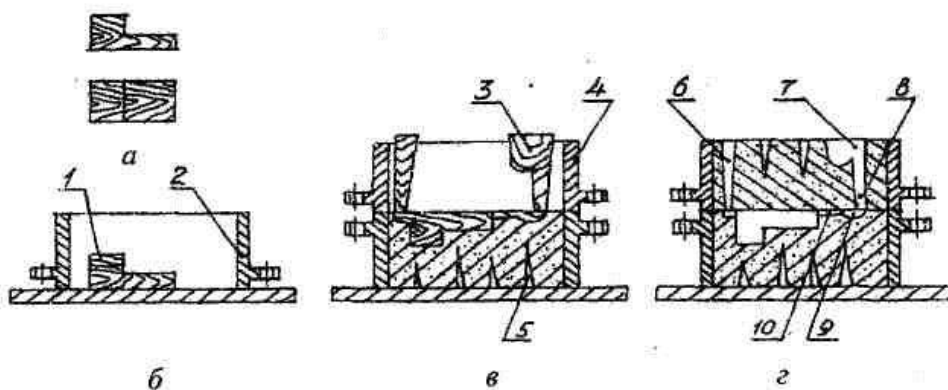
Последовательность операций при формовке в двух опоках по неразъемной модели: а – модель отливки; б, в – изготовление нижней и верхней полуформ; г – форма в сборе; 1 – модель отливки; 2 – нижняя опока; 3 – модель литниковой системы; 4 – верхняя опока; 5 – вентиляционные каналы; 6 – выпор; 7 – литниковая чаша; 8 – стояк; 9 – шлакоуловитель; 10 – питатели
